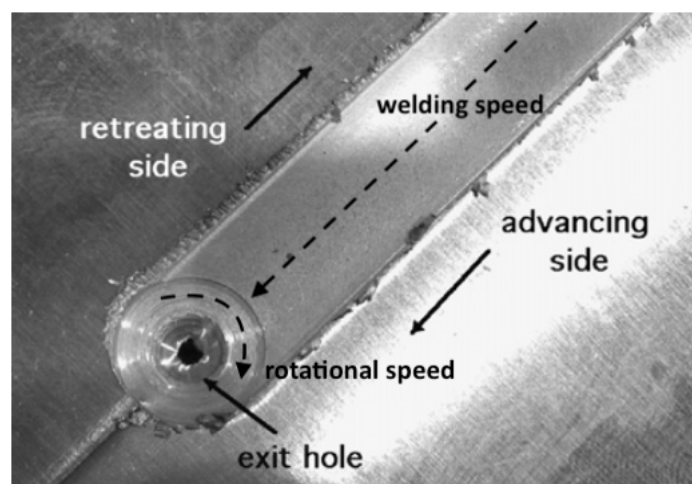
Lado de avance y retroceso en una soldadura FSW. [4]
